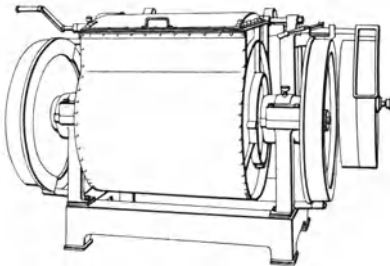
Mischmaschine für Grundseifenspäne (geschlossen).
